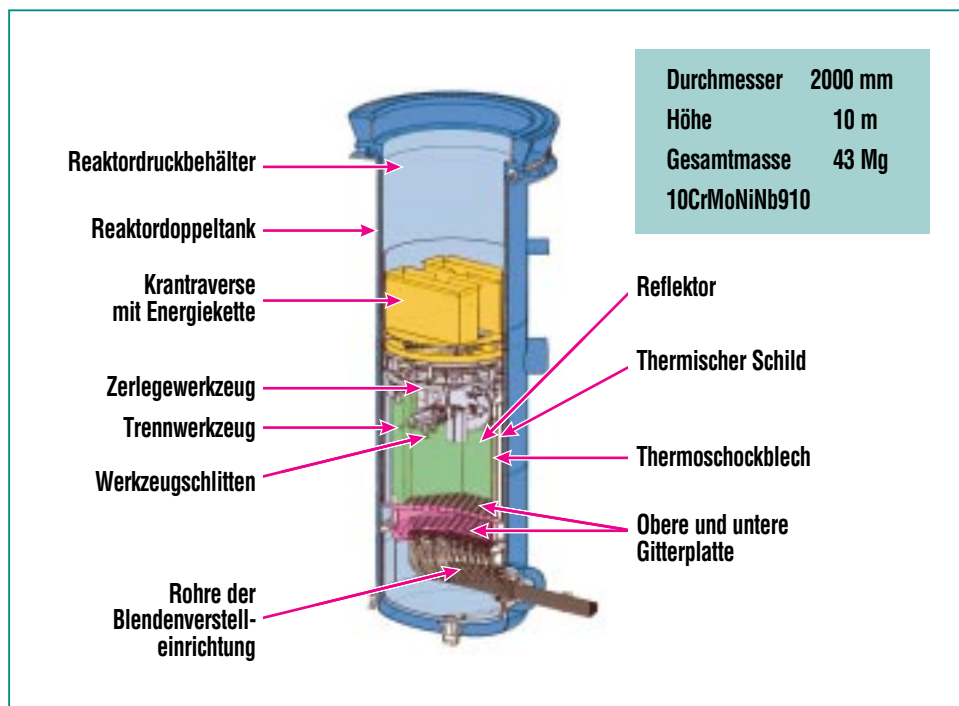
Reaktortank mit Einbauten und Zerlegewerkzeug.
